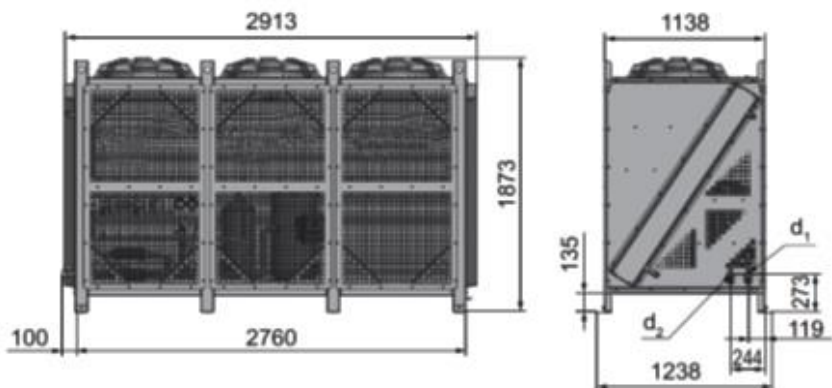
Загальний вид агрегату типу МАКК-120-241, МАКК-120-951
